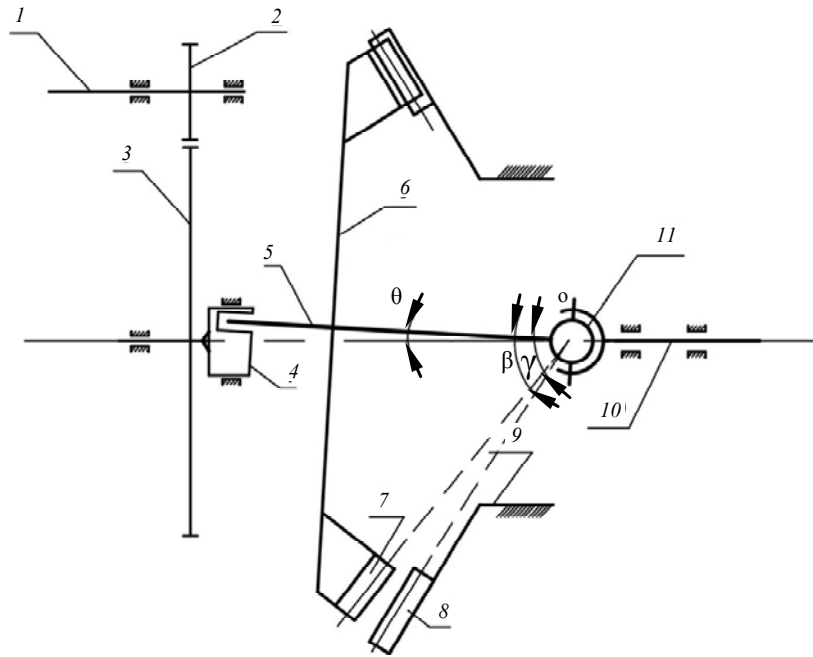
Кинематическая схема двухступенчатого редуктора, состоящего из эвольвентной косозубой и прецессионной передач:
